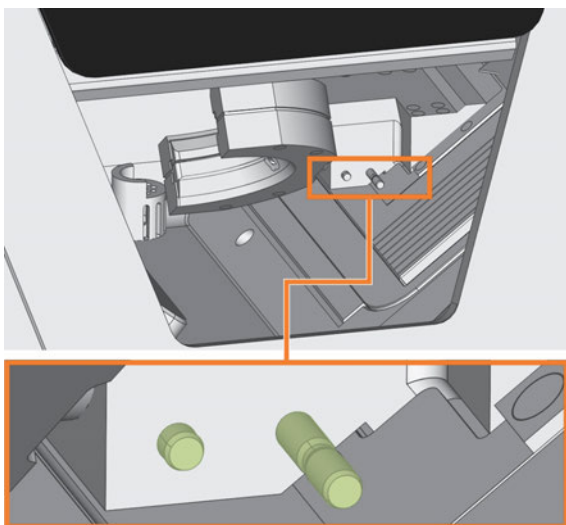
I BULLONI DEL PORTA-UTENSILI DI FRESATURA (VERDE)
